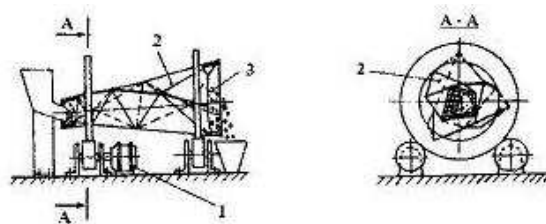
Схема предлагаемой конструкции установки на базе релятивного винтового барабана РК 5.1.а
